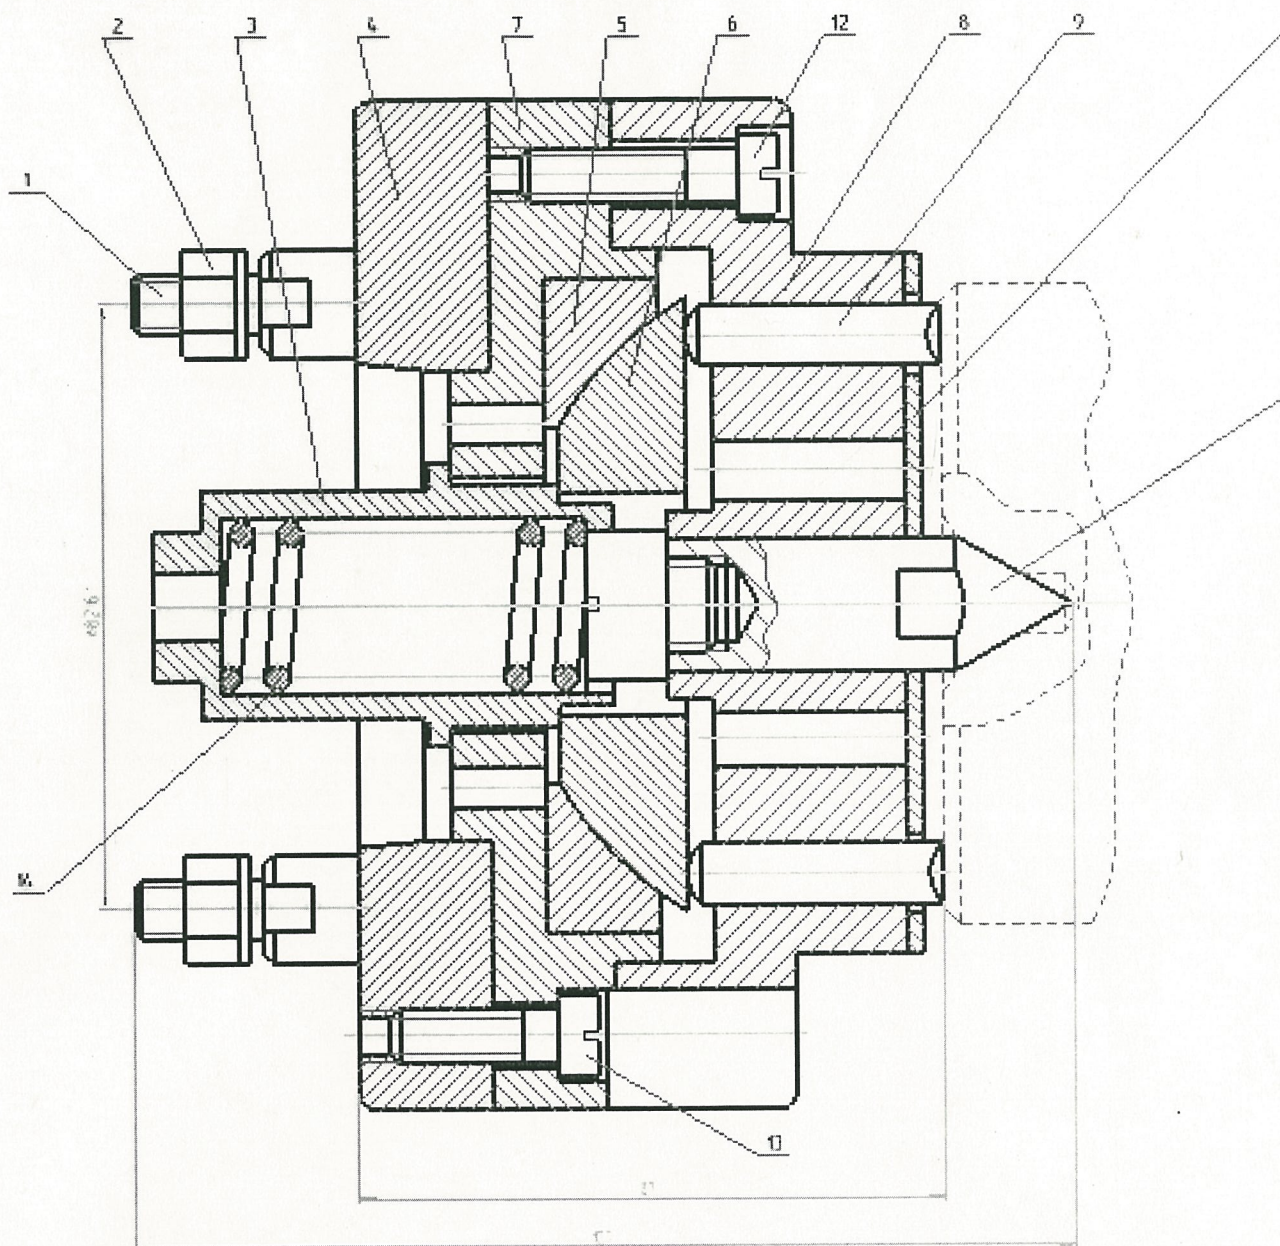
Повідковий патрон для тонкої токарної обробки валу
